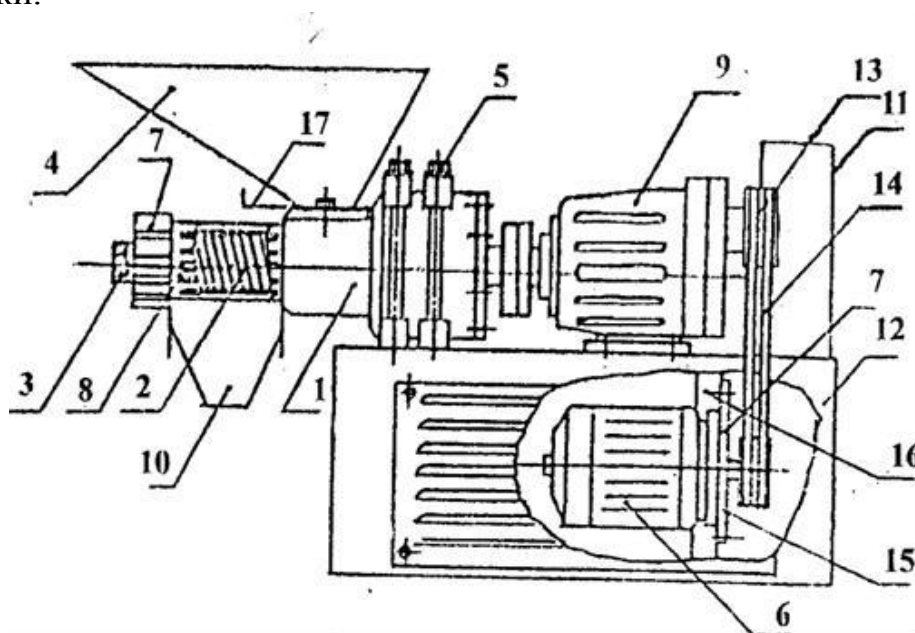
Прес-екструдер: 1 - корпус; 2 - шнек; 3 - насадка; 4 - бункер; 5 - болти; 6 - електродвигун; 7 - гайка накидна; 8 - голівка; 9 - редуктор; 10 - лоток;
